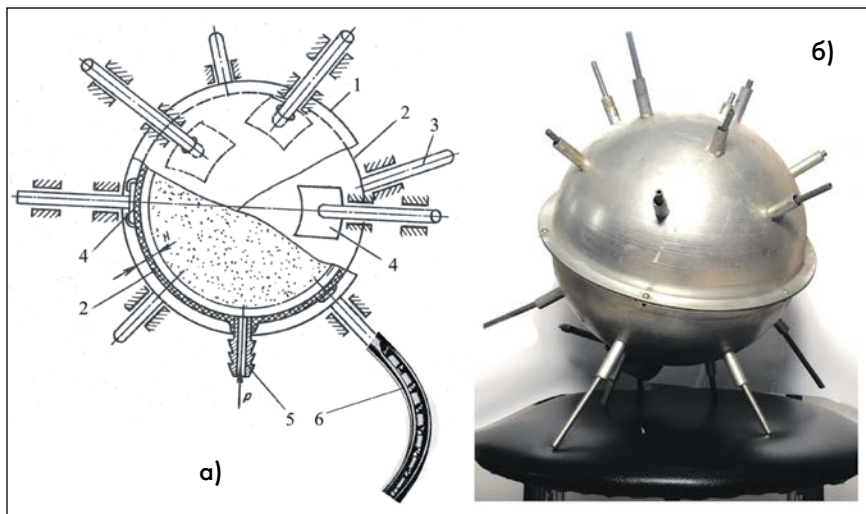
Исполнительный механизм: а) схема, б) общий вид
